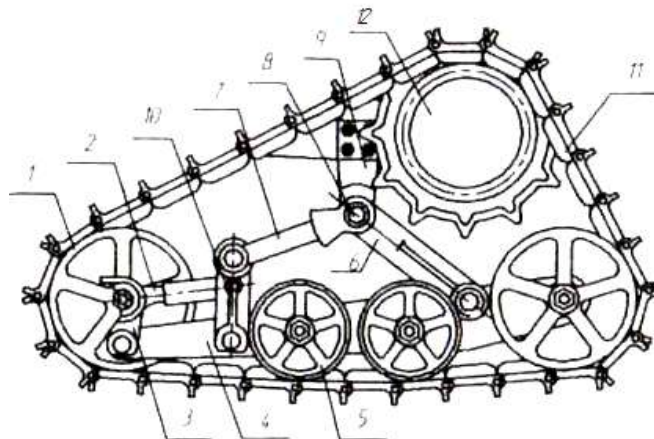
Полугусеничный движитель с жёстко закрепленными опорными катками
